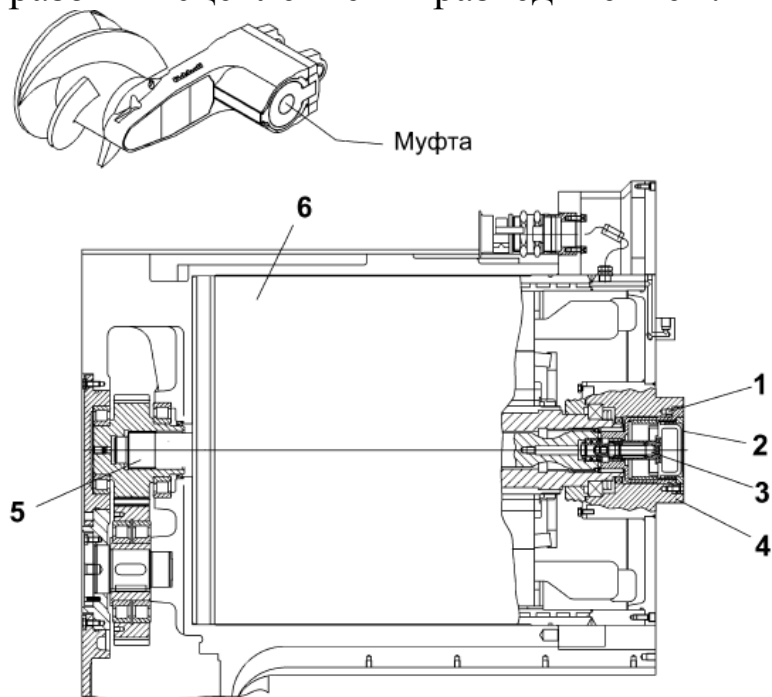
Муфта электродвигателя поворотного редуктора
